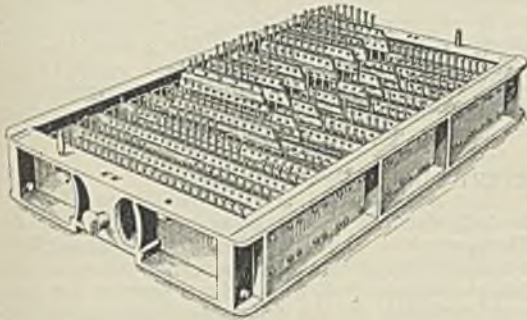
Formkasten (Oberkasten) zur Schwerkraft-Formmaschine.
